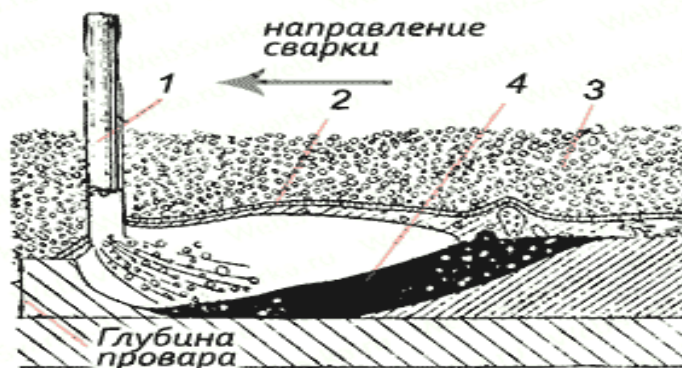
Сечение зоны горения дуги при сварке под флюсом
